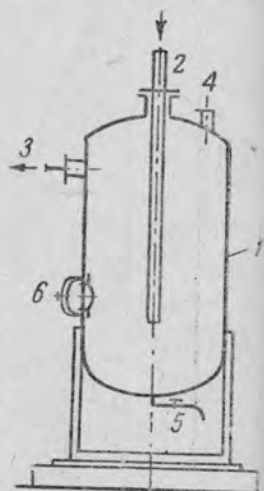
Ресивер: 1 — ресивер; 2 — воздушная труба от компрессора; 3 — труба на ресивер к шлиту управления; 4 — штуцер для предохранительного клапана; 5 — отверстие для спуска конденсата; 6 — люк.
